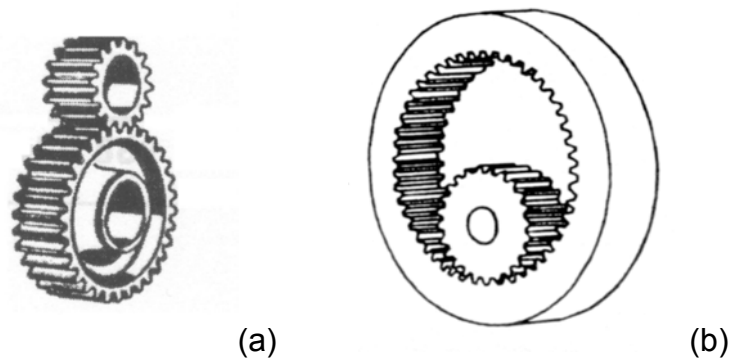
Engrenagens cilíndricas de dentes retos com engrenamento externo (a)^[12] e interno (b)^[13]
